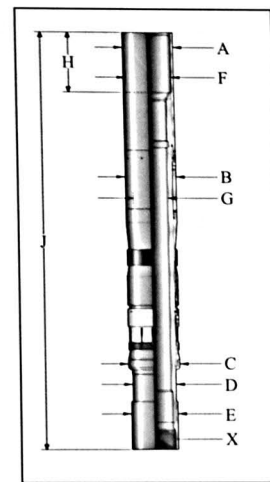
ZXP Верхний пакер подвески с уплотнительным элементом:
